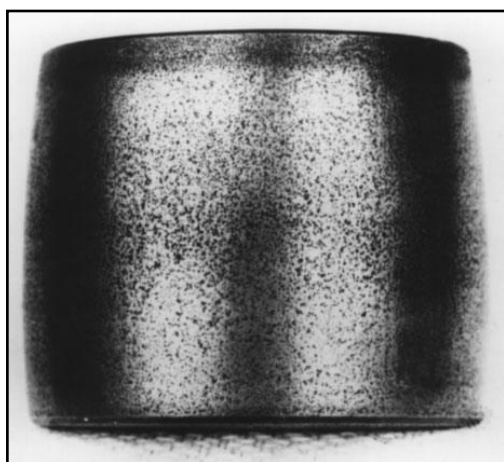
Componente de um rolamento de aço após ação do desgaste corrosivo
